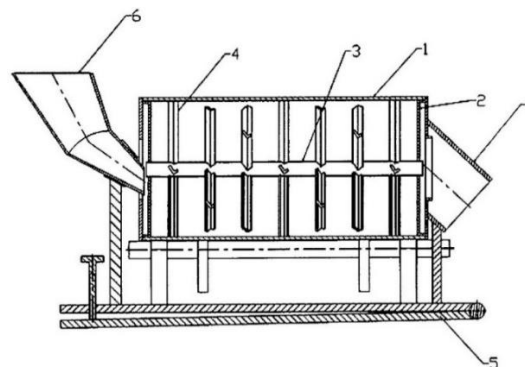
Барабанный смеситель с Г-образными лопастями
